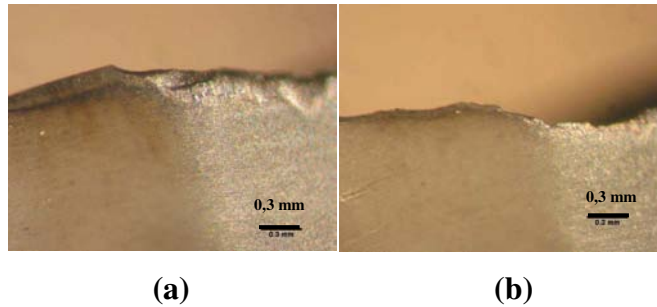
Ensaio 10.1 (a) e ensaio 10.1 (b). Arestas de corte utilizadas nos ensaios com ferramentas de cerâmica sem cobertura. Fim da vida da ferramenta
